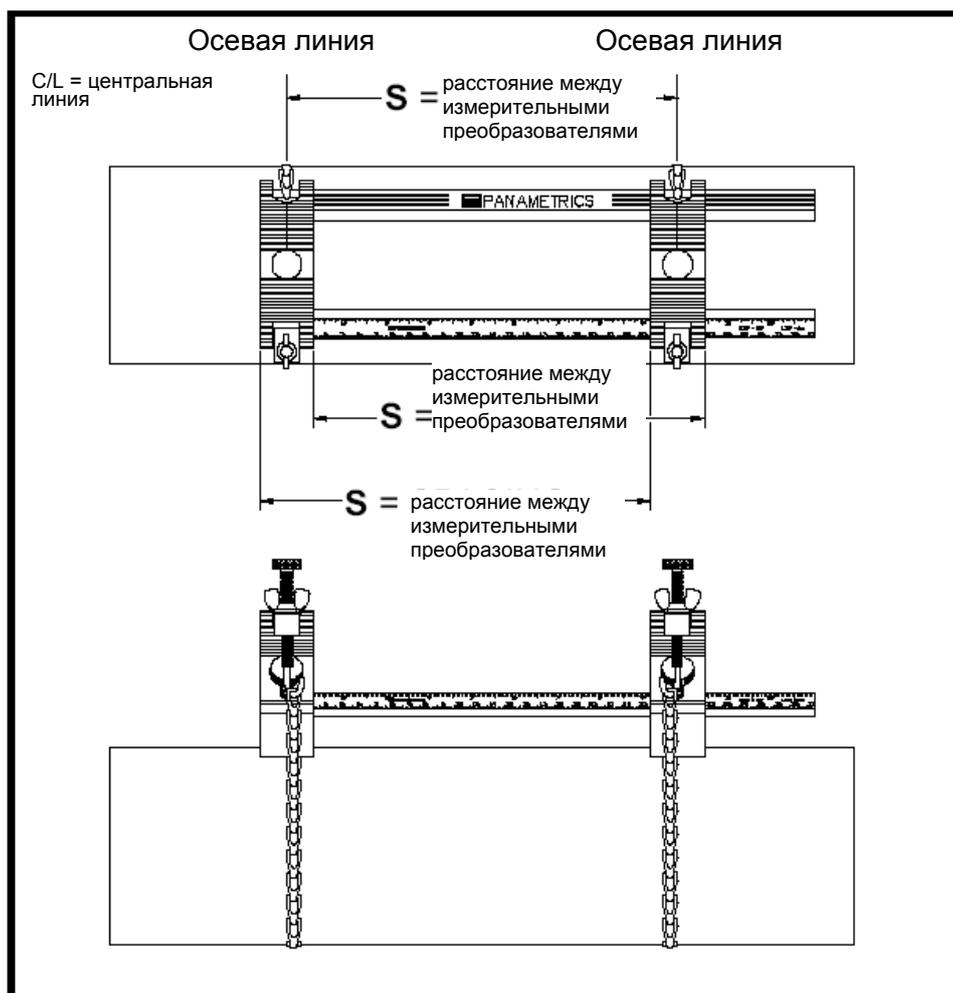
Установка крепежного приспособления для двухходового метода измерения
